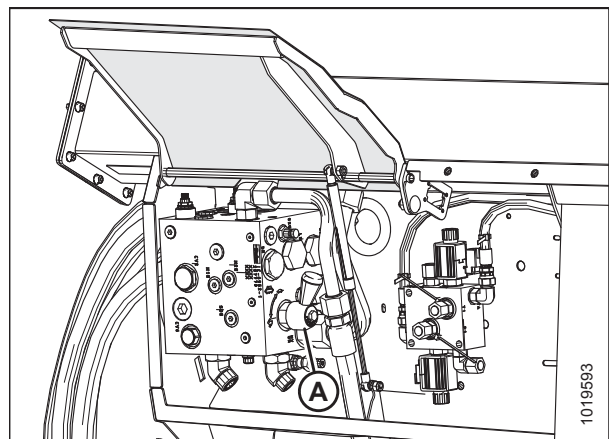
Pokrywa przedziału hydraulicznego
